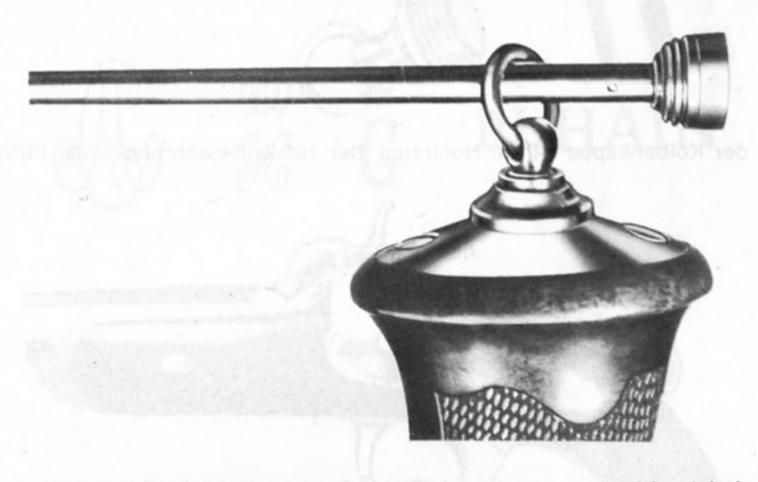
Die Fangriemenöse läßt sich nach oben schieben und wirkt dabei als Steckschlüssel für den eingeschraubten Deckel der Kolbenkappe
